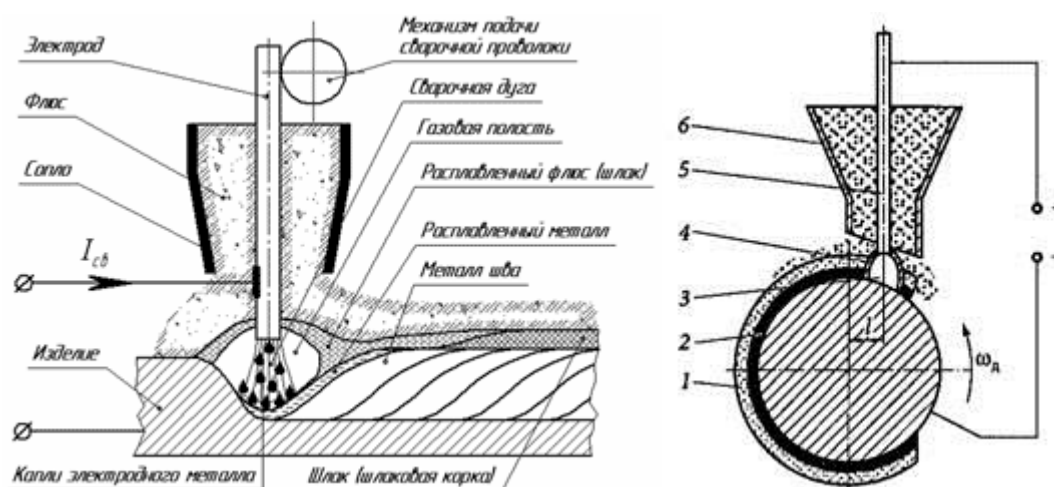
Схема наплавки под слоем флюса: 1 - шлаковая корка; 2 – наплавленный металл (металл шва); 3.- газовая полость; 4 -расплавленный флюс (эластичный мешок); 5 -электродная проволока; 6.-бункер флюса
